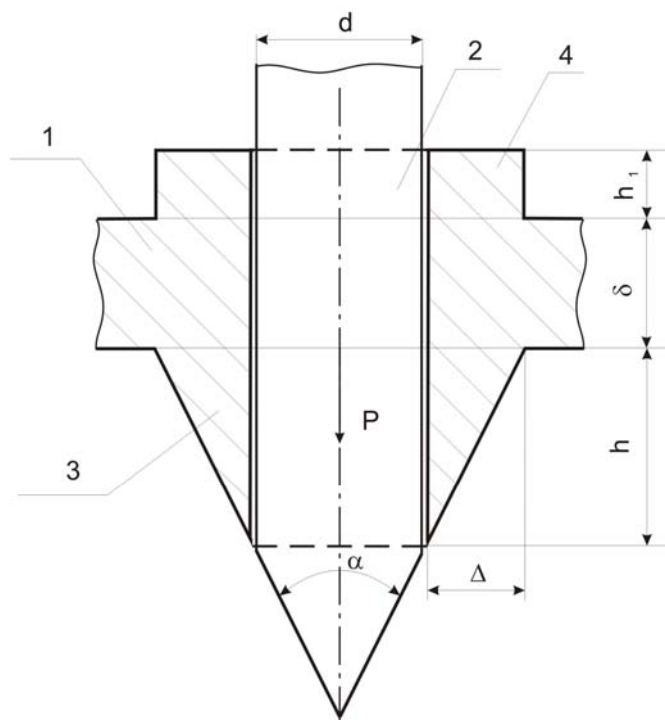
Схема отбортовки: 1 – деталь; 2 – пуансон; 3 – конусная втулка; 4 – кольцо
